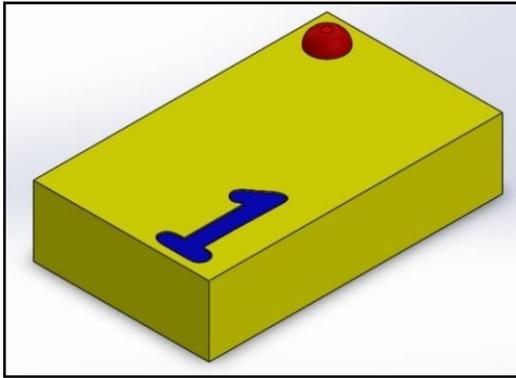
Vista de planta de ficha seleccionada. [Autores].
